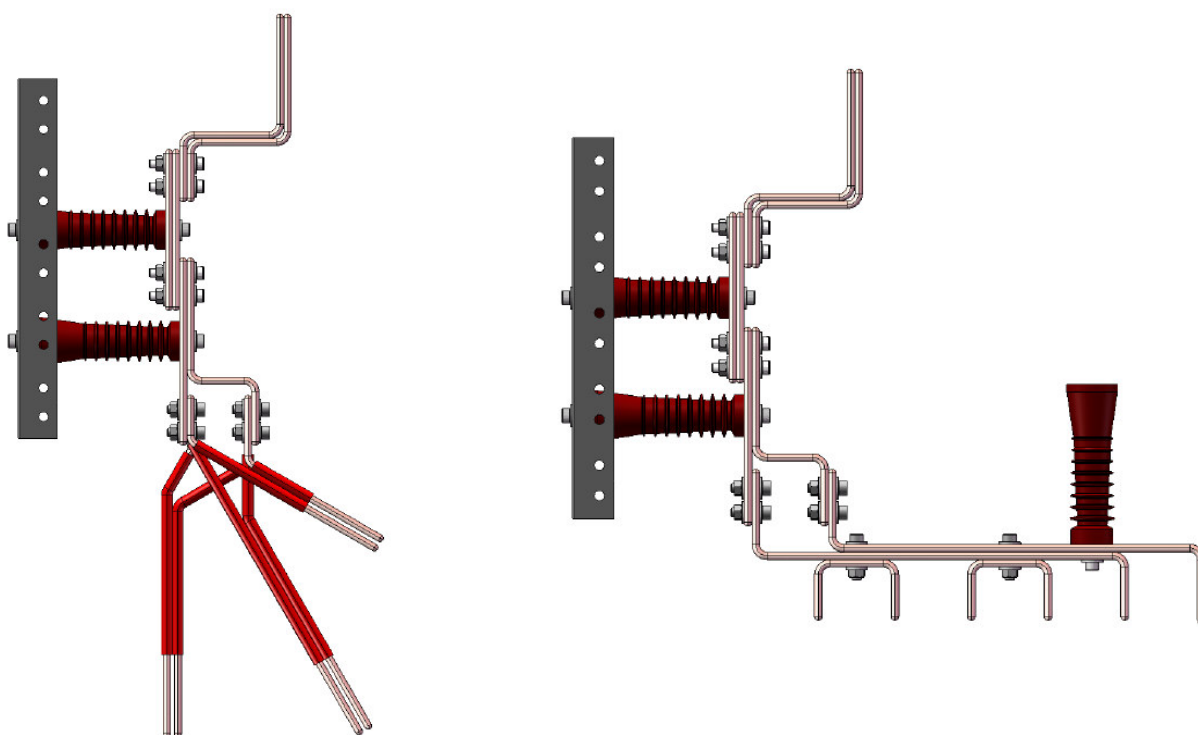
Confronto tra due preassemblaggi quello a sinistra provvisto di congiuntore e quello a destra equipaggiato con le sbarre per allacciare i cavi
